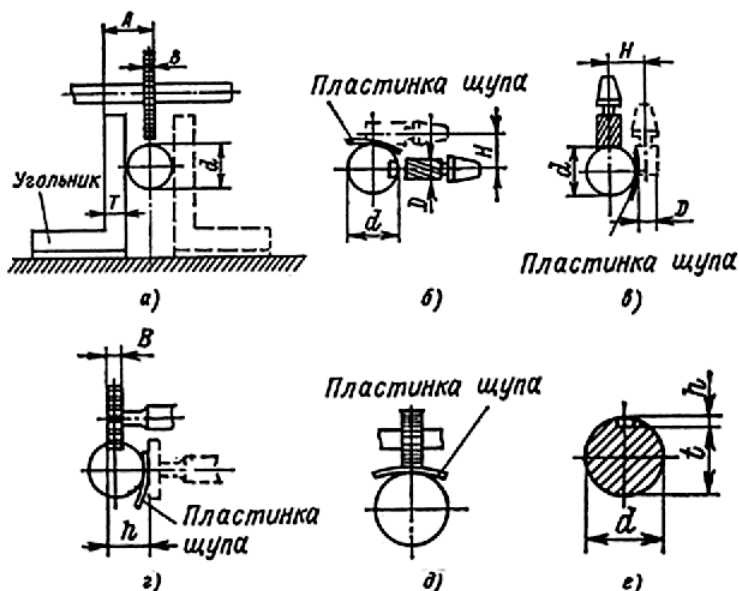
Схемы настройки станков для фрезерования шпоночных пазов
